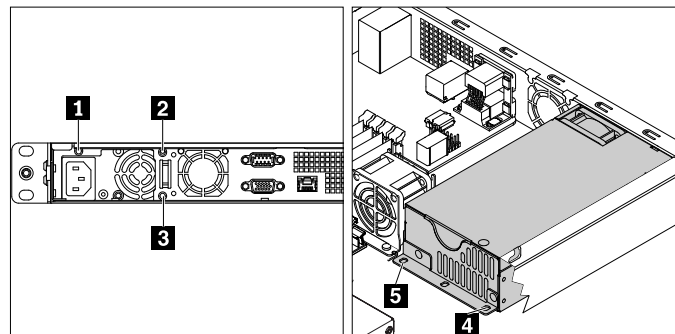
Befestigungsschrauben für das neue Netzteil anbringen
